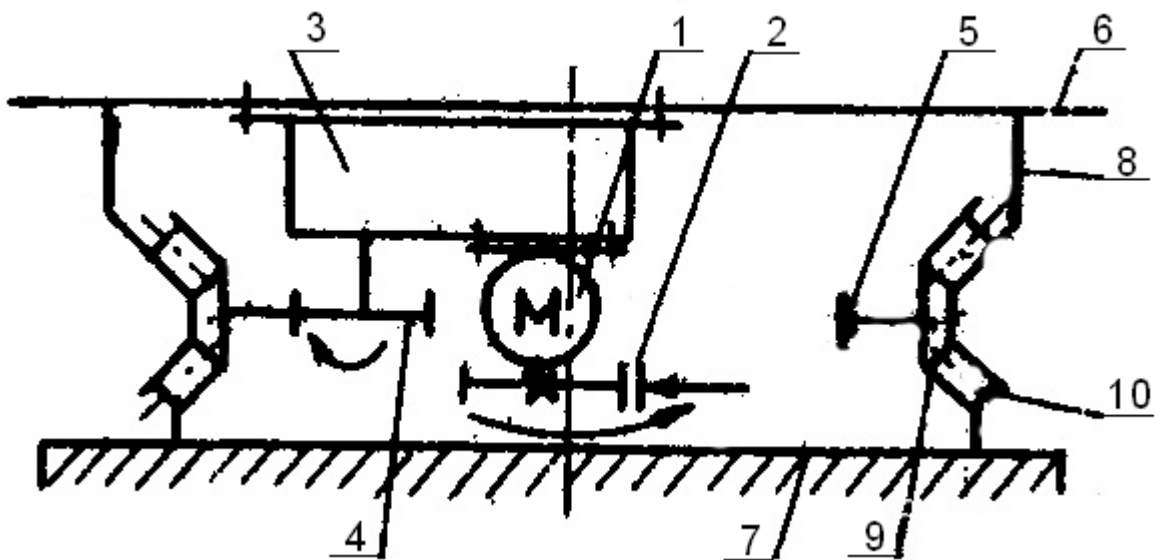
Схема пристрою для обертання поворотної платформи
